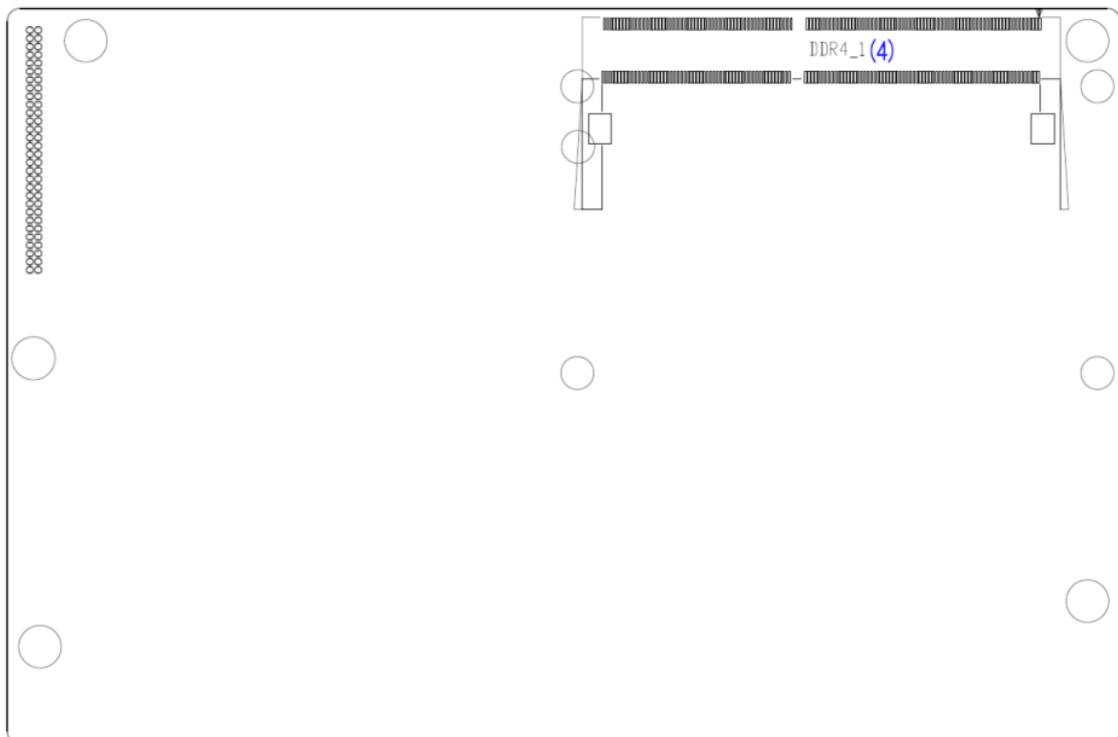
Jumper und Anschluss – Board Rückansicht
